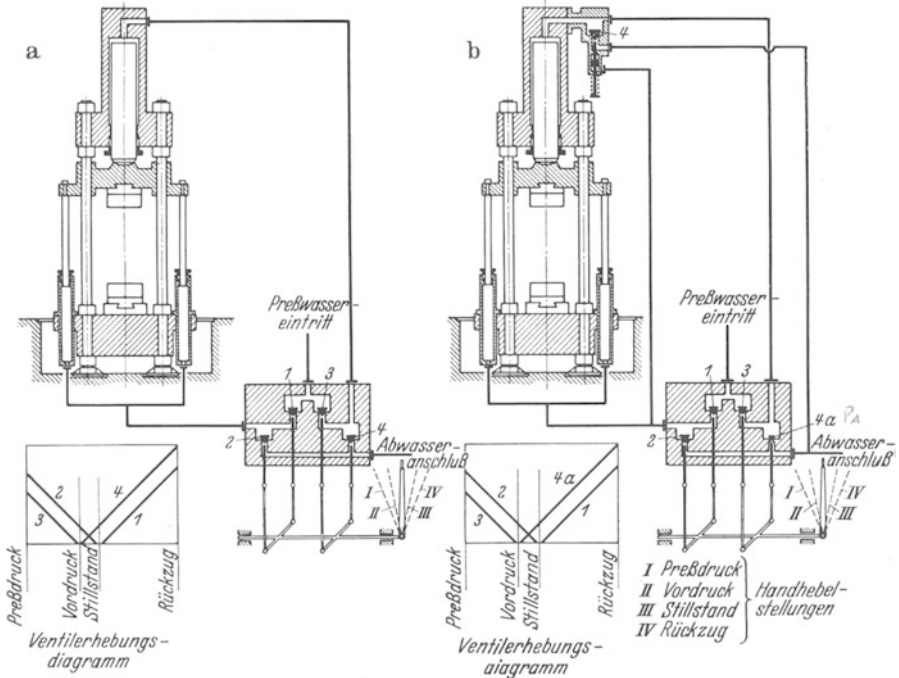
a u. b. Steuerschema für eine reinhydraulische Einzylinderschmiedepresse.
